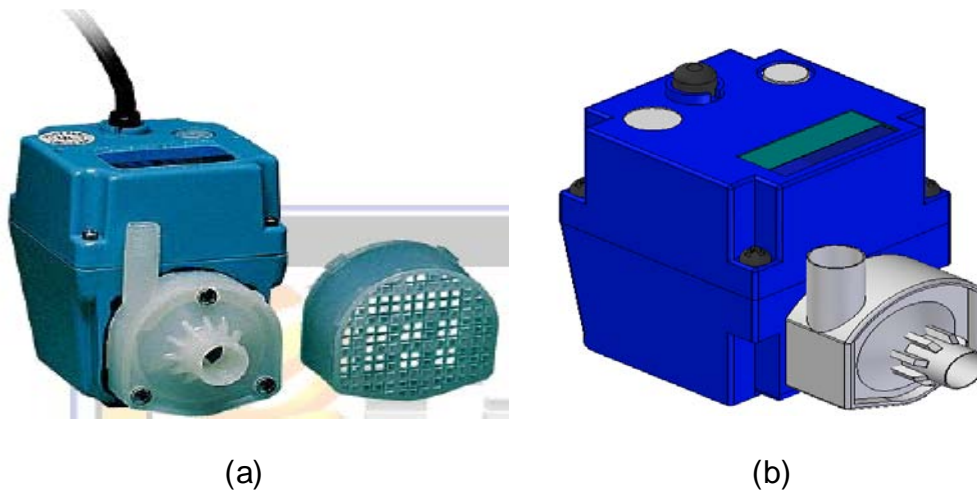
(a) Bomba Centrífuga [31], Diseño en Solid Edge
